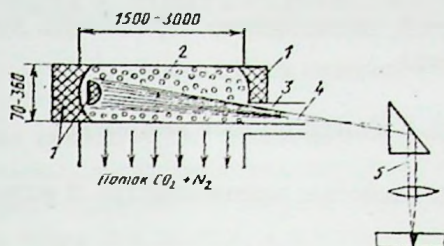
Схема установки для лазерной сварки с газовым лазером:
